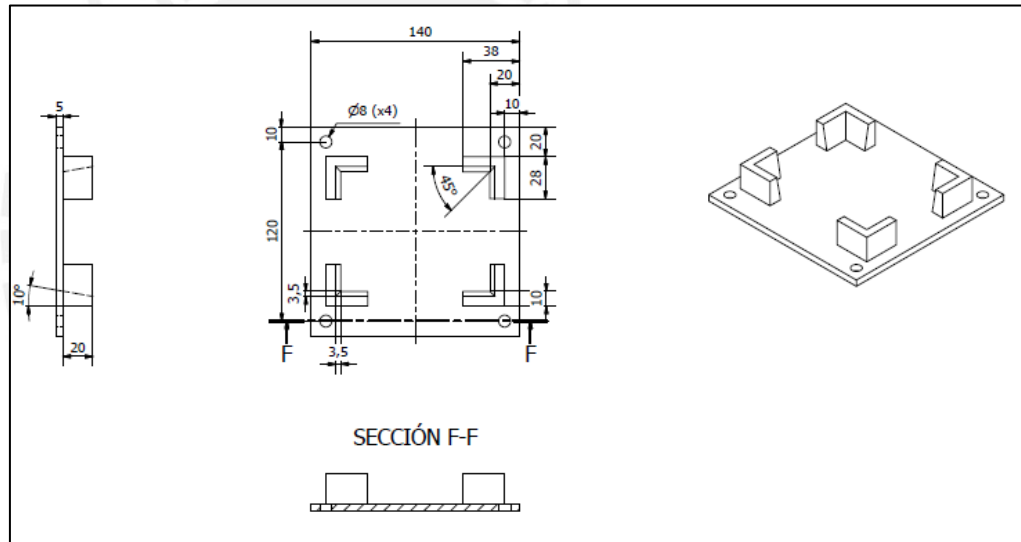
Mesa de Trabajo - Vistas, detalles y secciones
